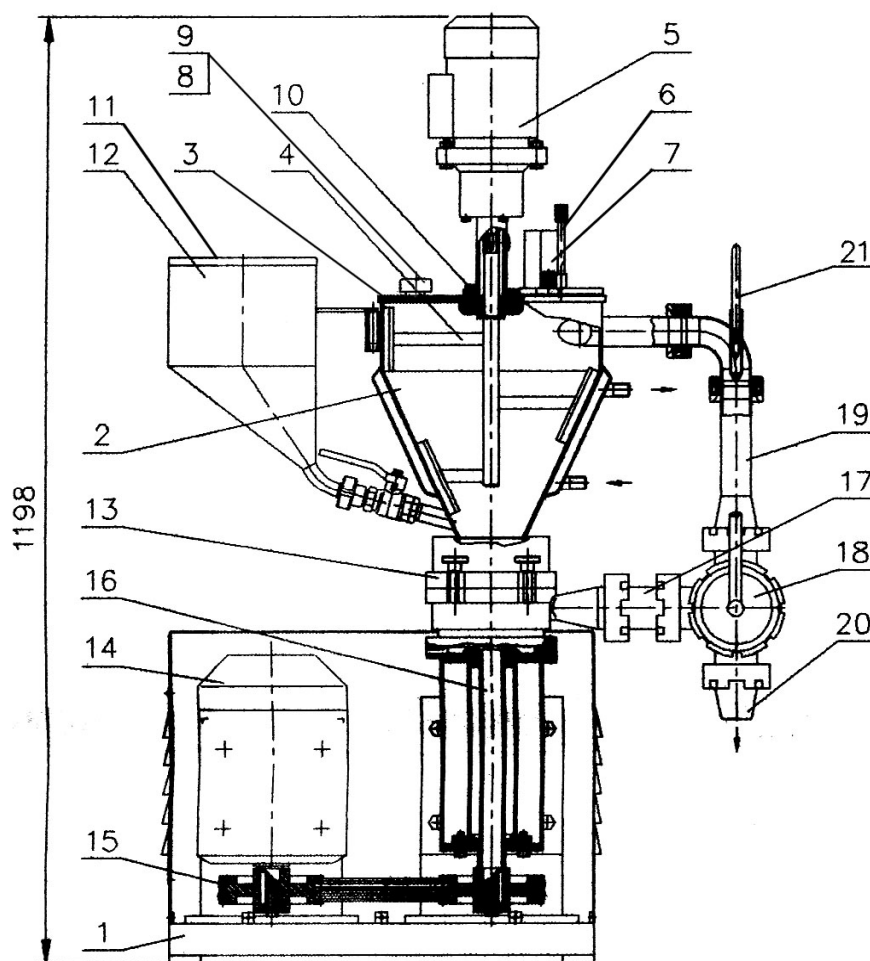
Апарат марки Я5-ОЭВ для змішування і термічної обробки продуктів: 1 – станина; 2 – робоча місткість; 3 – верхня кришка; 4 – скребкова мішалка; 5 – привід мішалки; 6 – вікно для контрольних оглядів; 7 – мановакуумметр; 8 – запобіжний клапан; 9 – патрубок; 10 – ущільнення; 11, 12 – бункери рецептурних компонентів; 13 – пристрій подрібнювально-транспортуючий; 14 – привід подрібнювача; 15 – пасова передача приводу подрібнювача; 16 – блок вала проміжного; 17 – патрубок; 18 – вентиль триходовий; 19 – циркуляційний контур; 20 – патрубок виходу готового продукту; 21 – датчик температури.
